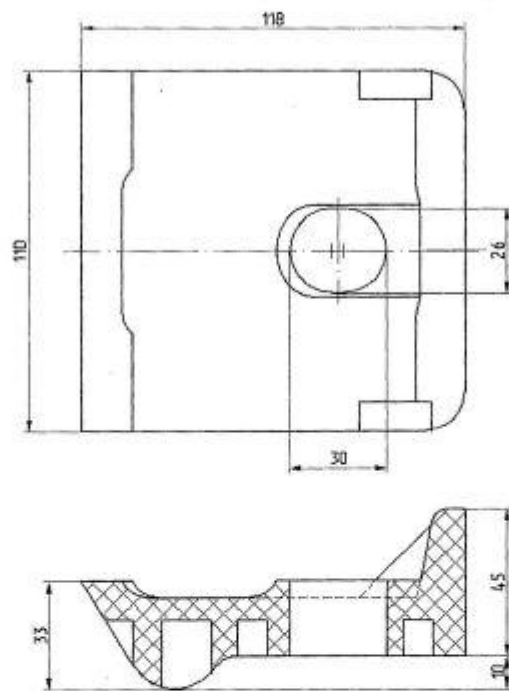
Упор боковой полимерный ЖБР для креплений
